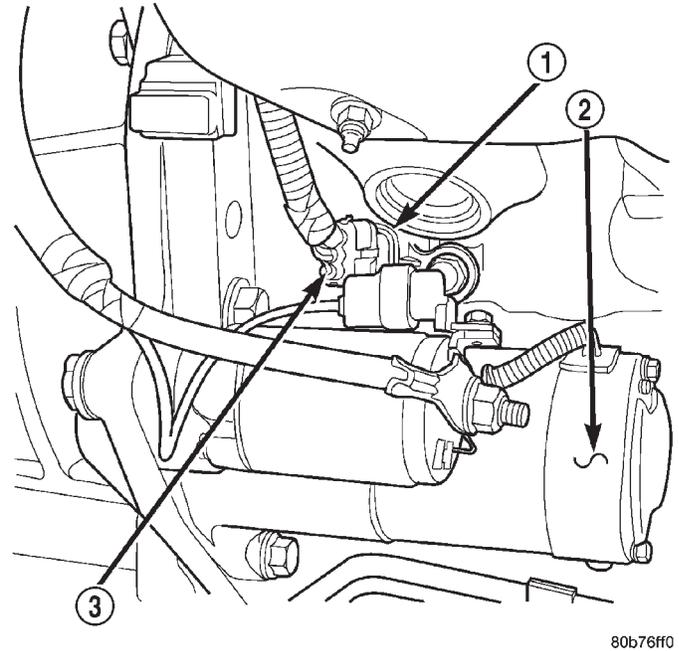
Kurbelwinkelgeber (CKP)—4.7L-V8-Motor
